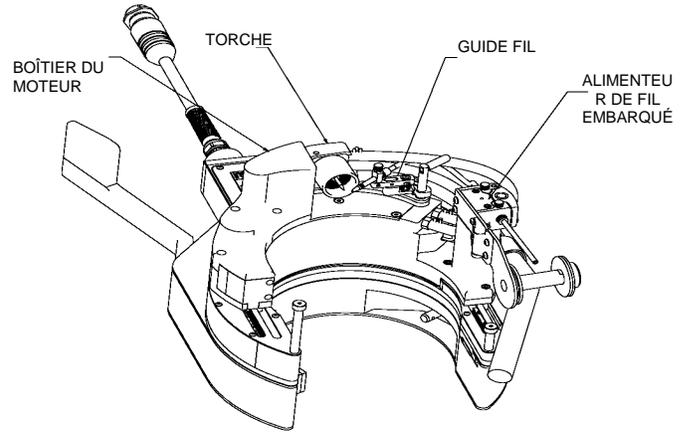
Ensemble de mouvement Ensemble de guide fil
